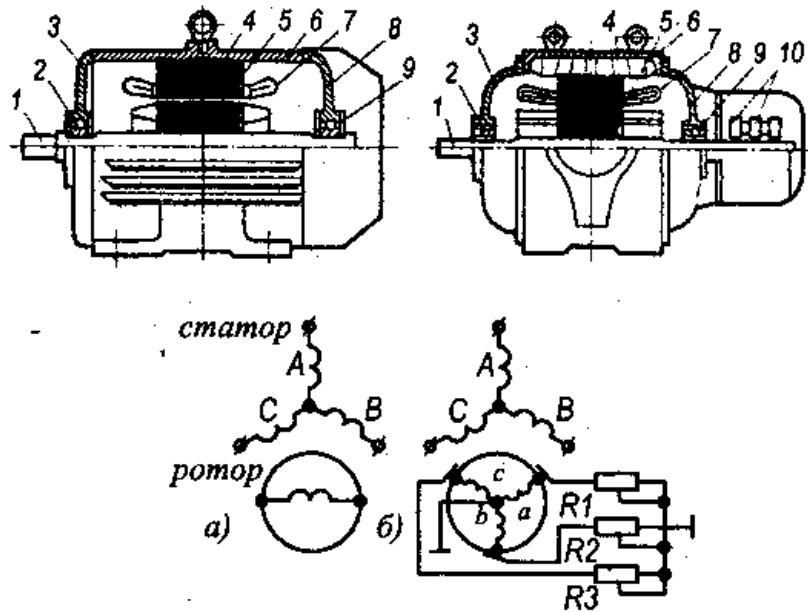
Устройство и схемы включения асинхронных двигателей: а — с замкнутым ротором; б — с разомкнутым ротором; 1 — вал; 2, 9 — подшипники; 3, 8 — подшипниковые щиты; 4 — статор; 5 — ротор; 6 — корпус; 7 — фазная обмотка; 10 — контактные кольца подключения
